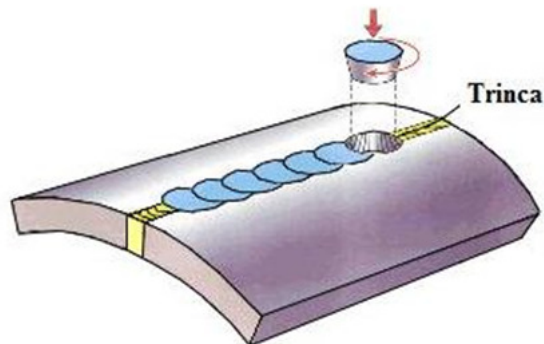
Soldagem tipo *Friction taper stitch welding*.
